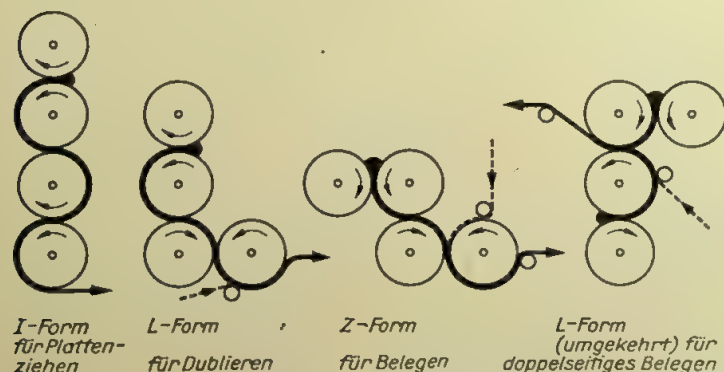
Gebräuchlichste Walzanordnungen bei Vierwalzenkalandern
